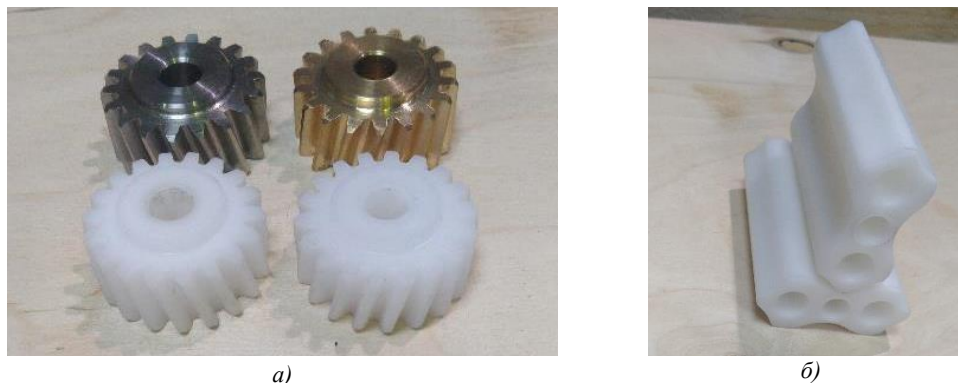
Синхронизирующие шестерни (а) и кулачковые роторы (б). *Fig.4. Synchronizing gears (a) and lobe rotors (b).
